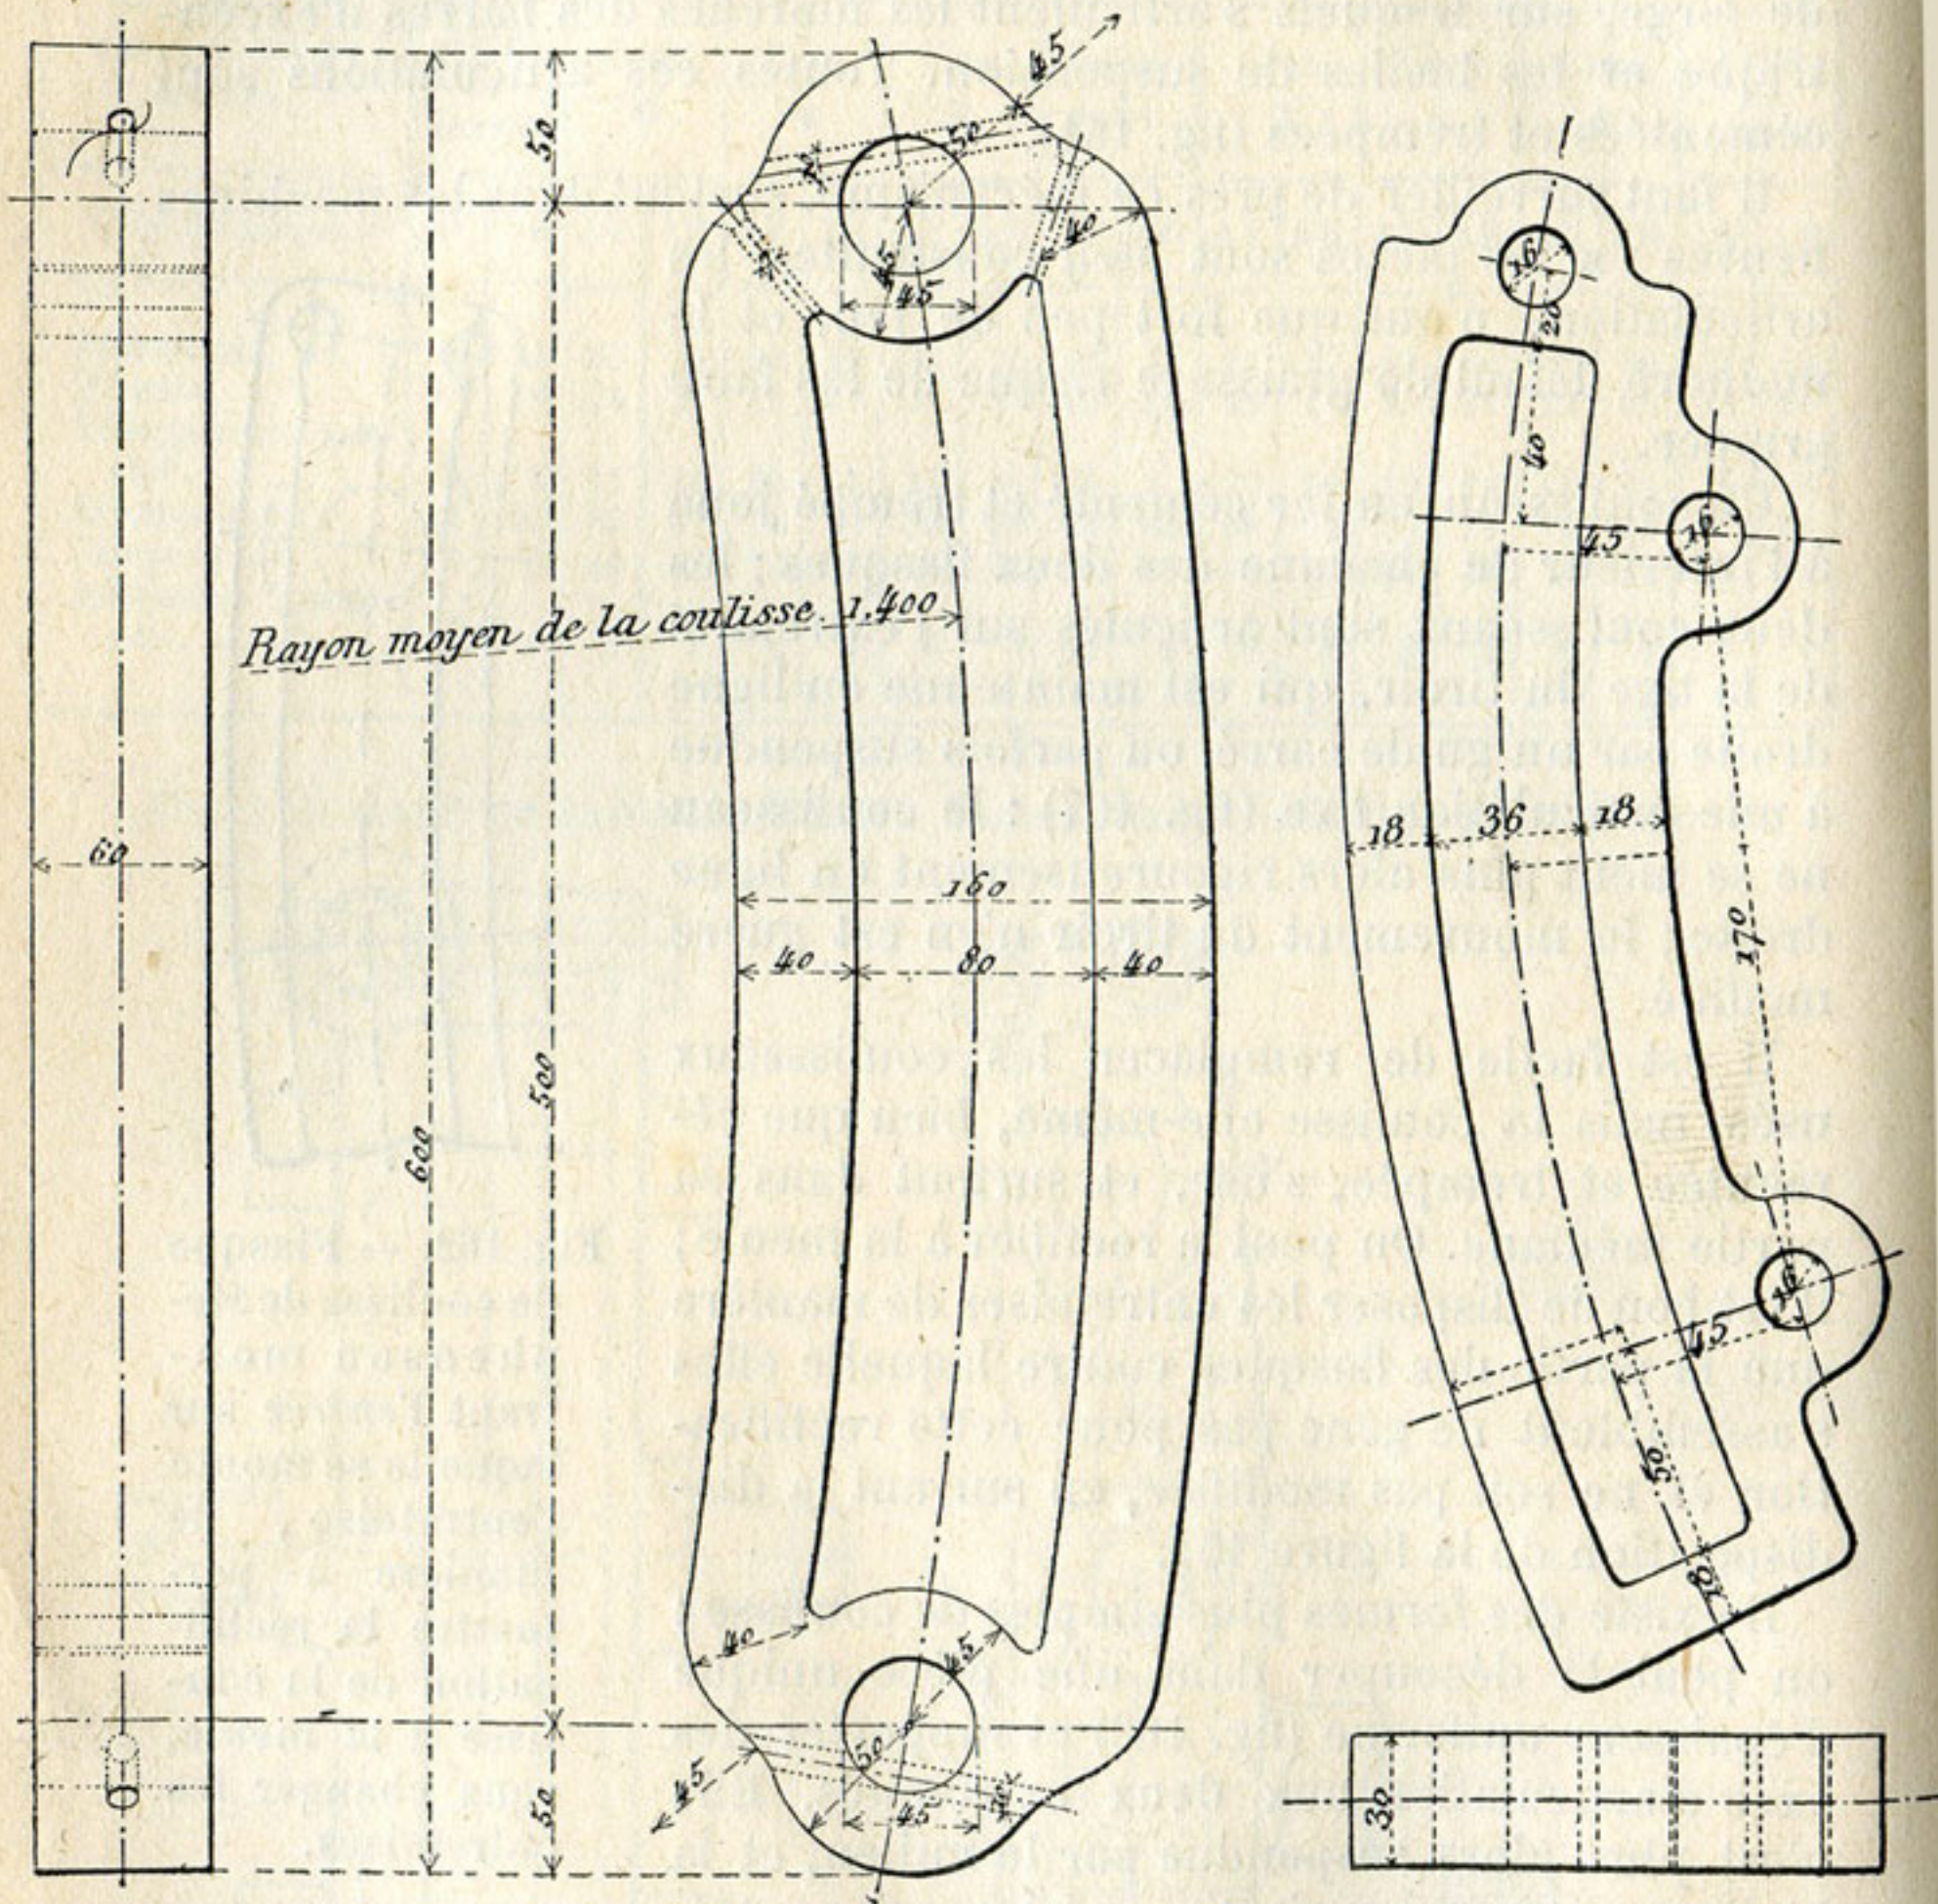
Coulisse de Stephenson découpée dans une pièce unique.
